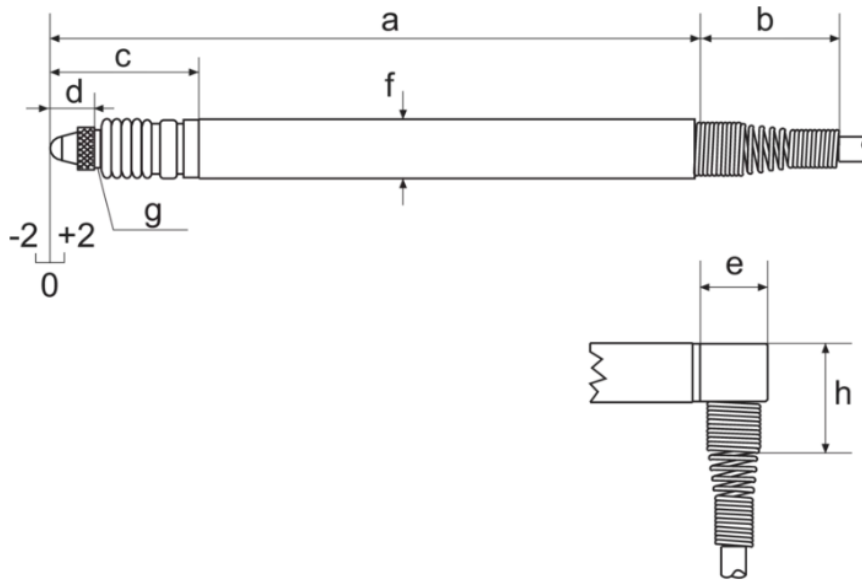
Dimensions del palpador inductiu Milimar P2004 M. [10]
